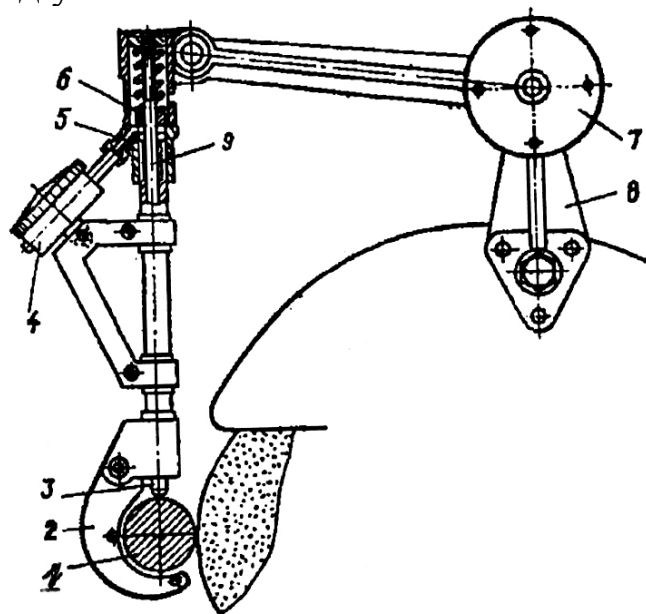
Пристрій для автоматичного контролю розміру шийки вала під час шліфування:
